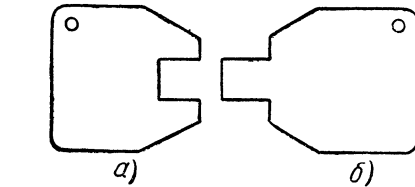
Установка резца при нарезании прямоугольной резьбы.
